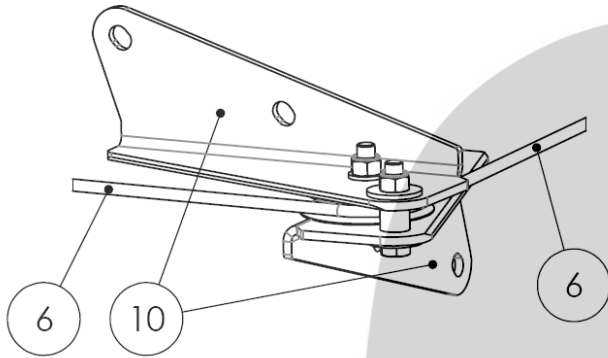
Método de montaje del cable a través de un punto de anclaje de esquina exterior.
